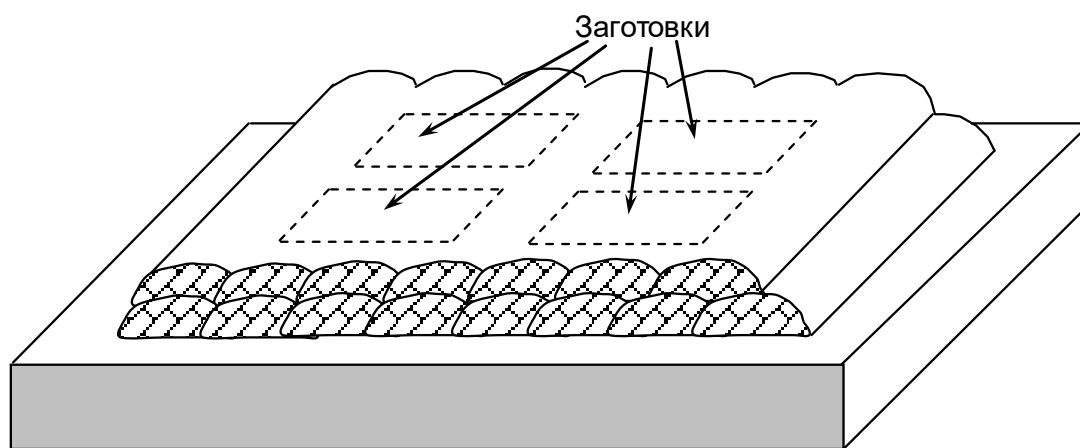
Схема наплавлення та місця відбору заготовок для зразків.
